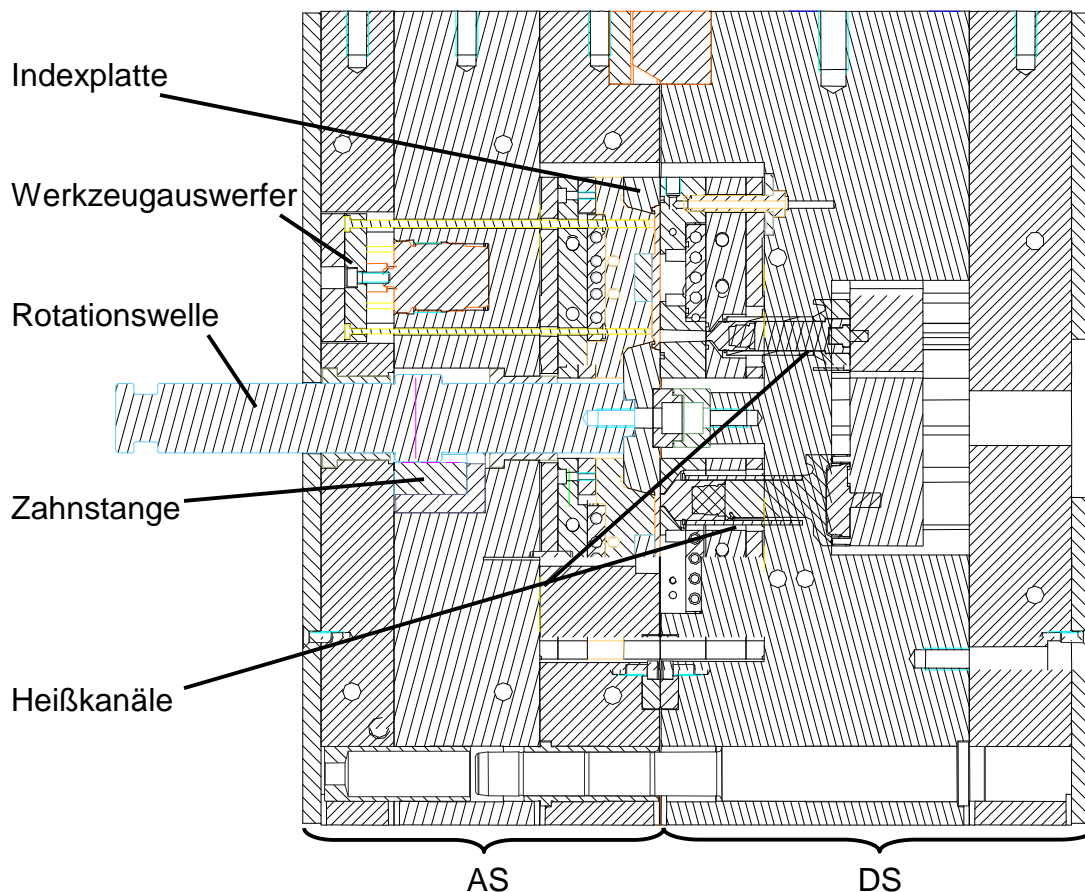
Querschnitt des Indexplatten-Werkzeuges für die galvanische Replikation
